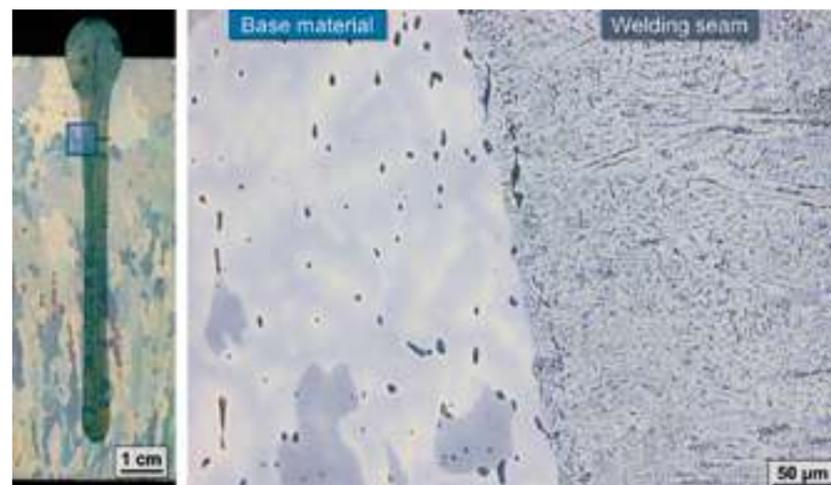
EB-Schweißnaht mit einem Gefügeausschnitt aus dem Übergangsbereich Grundwerkstoff/Schweißnaht (16-7-9)
